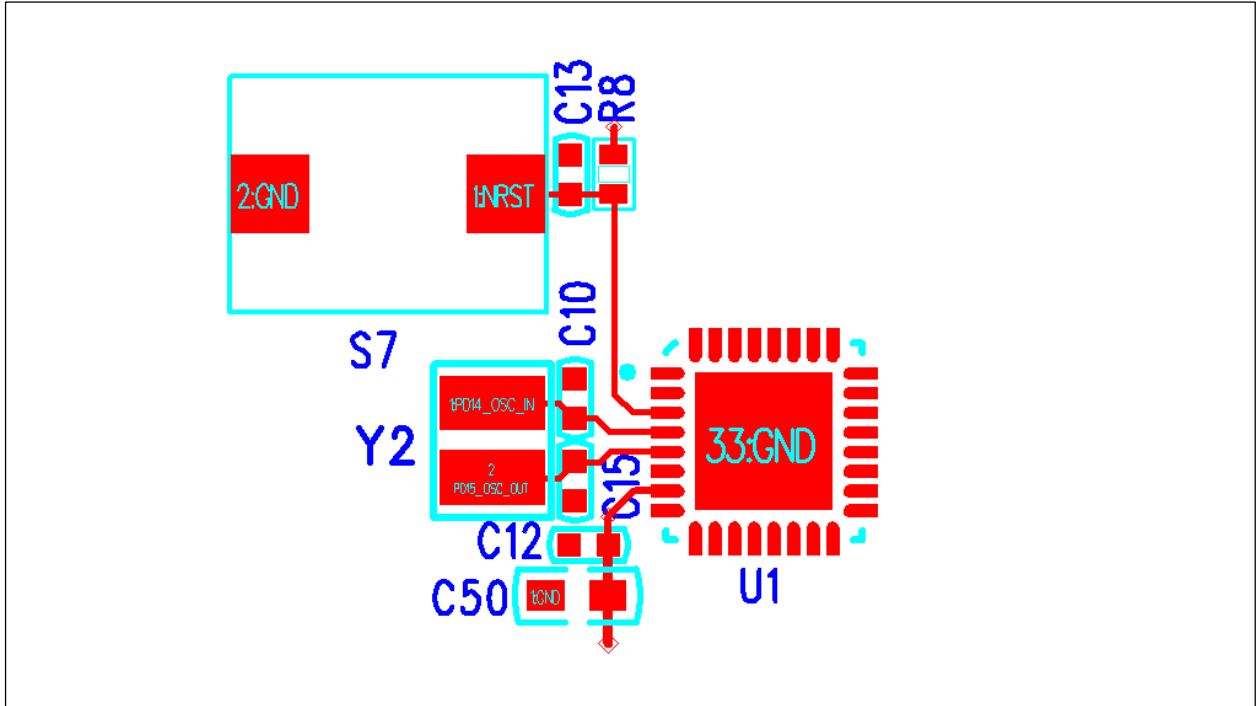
QFN32 封装 PCB LAYOUT 参考图
